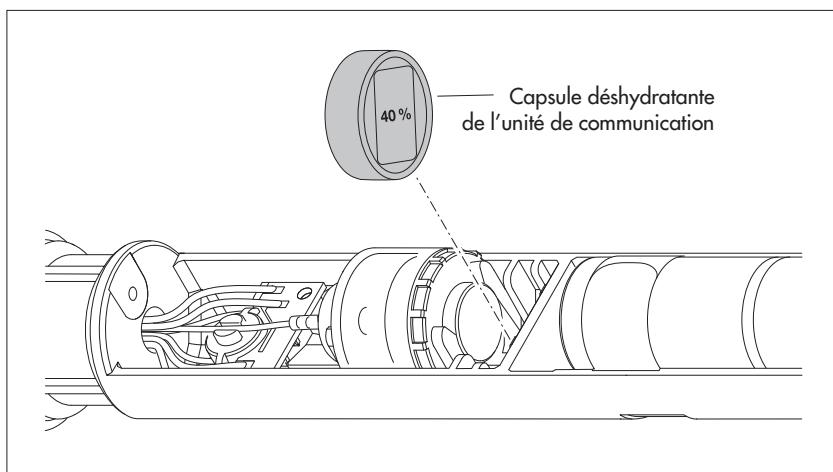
Remplacement de la capsule déshydratante de la sonde de pression.
